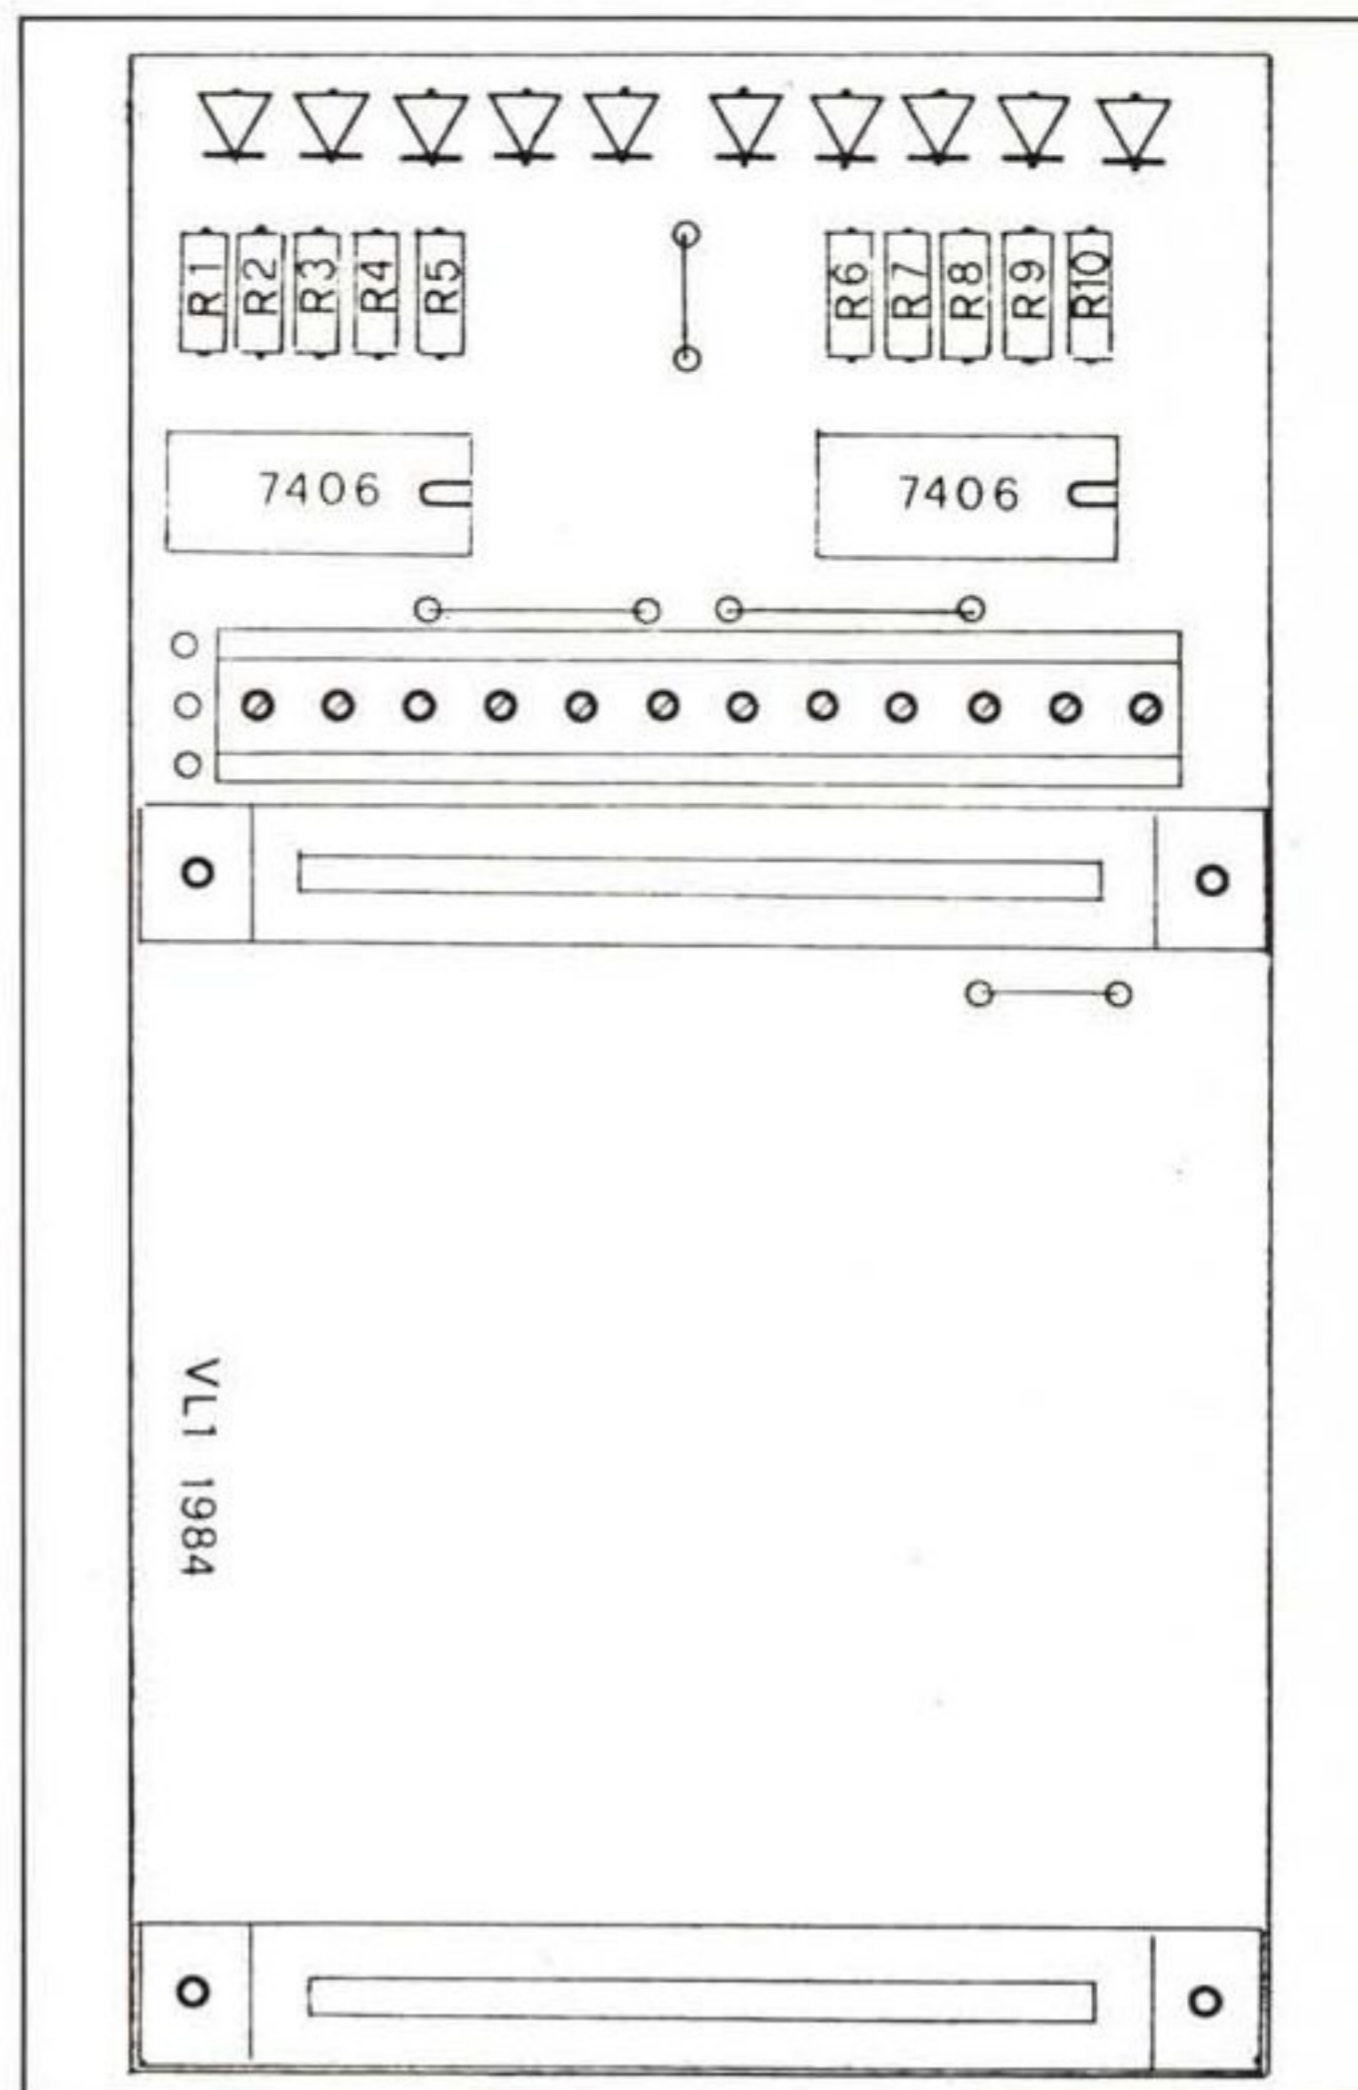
Assemblaggio dei componenti sul C.S. VLI.
